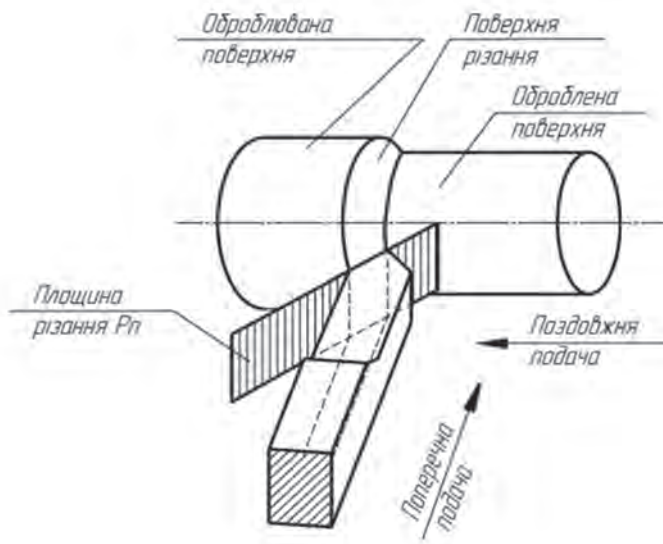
Види поверхонь на оброблюваній заготовці
